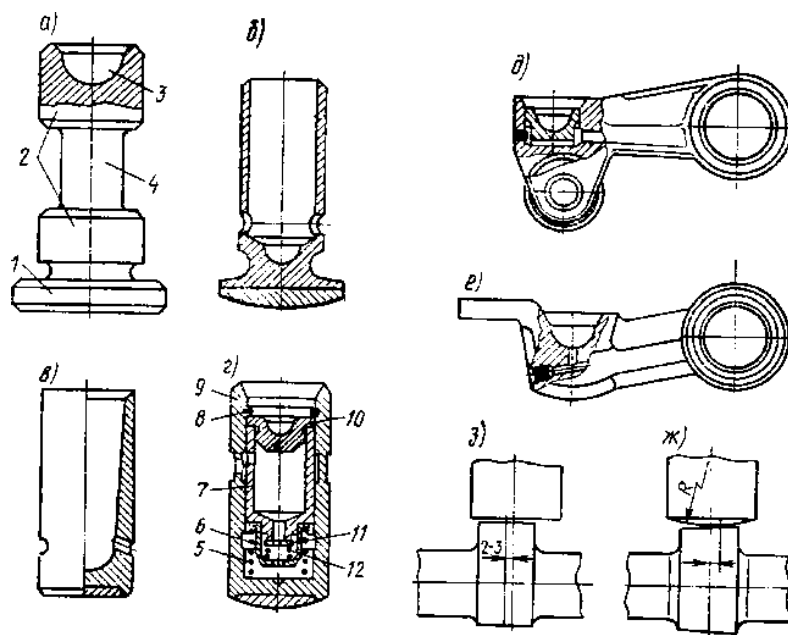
Штовхачі, а) тарілчастий; б) тарілчастий з проточкою під декомпресорний пристрій; в) циліндровий; г) гідравлічний; д) що коливається з роликом; е) пристрій, що коливається, ж і з) способи розміщення штовхачів щодо кулачка
